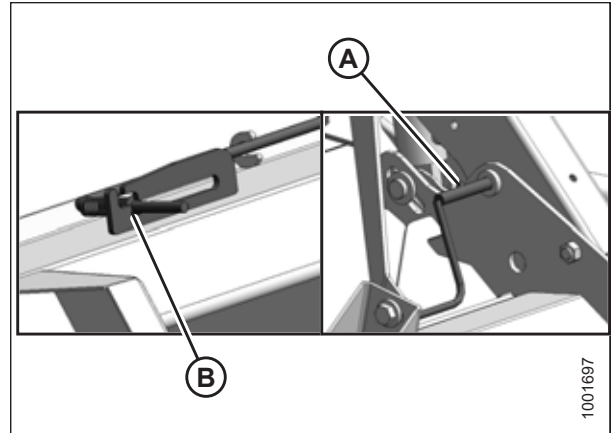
Запобіжний упор мотовила — центральний важіль
